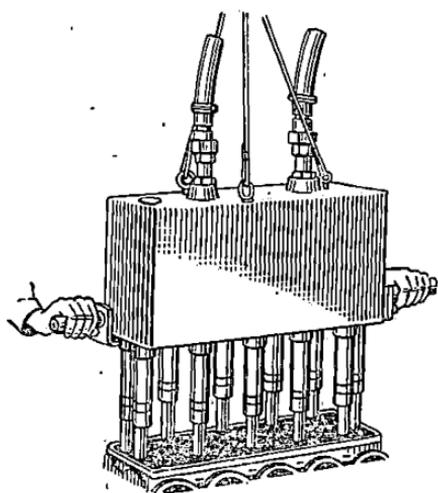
Многошпиндельный гайковерт для завинчивания гаек крепления головки цилиндра.
